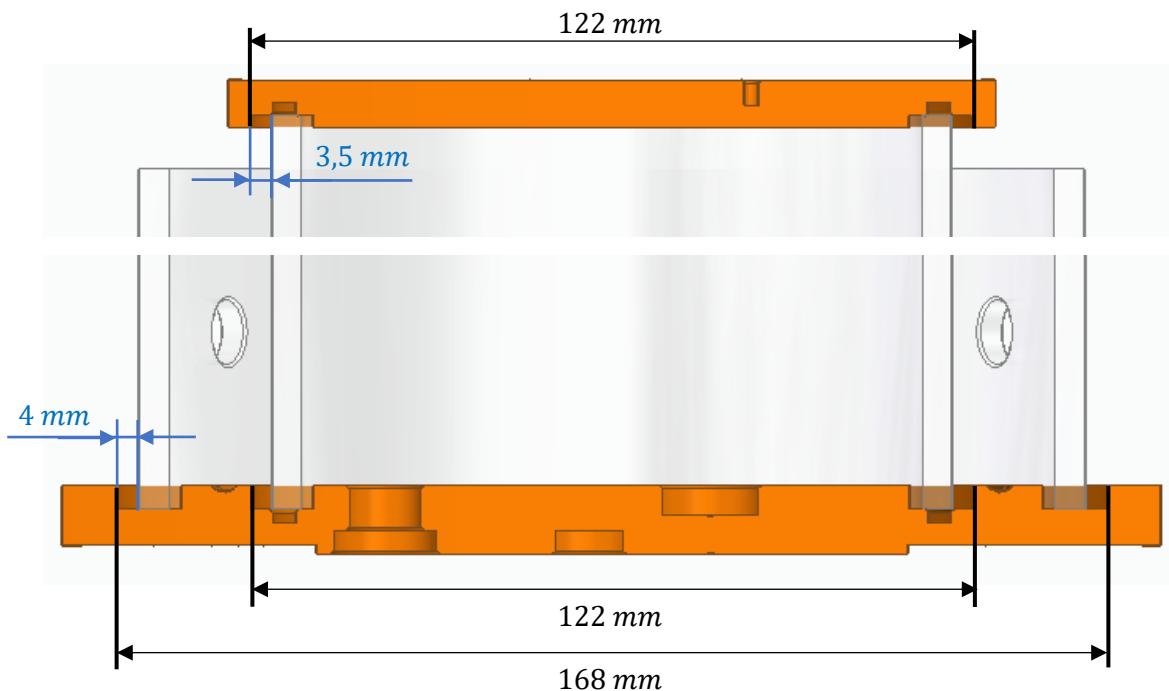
Schnittansicht von Boilerdeckel und -boden mit gewählten Außendurchmessern für die Zylinderausschnitte
